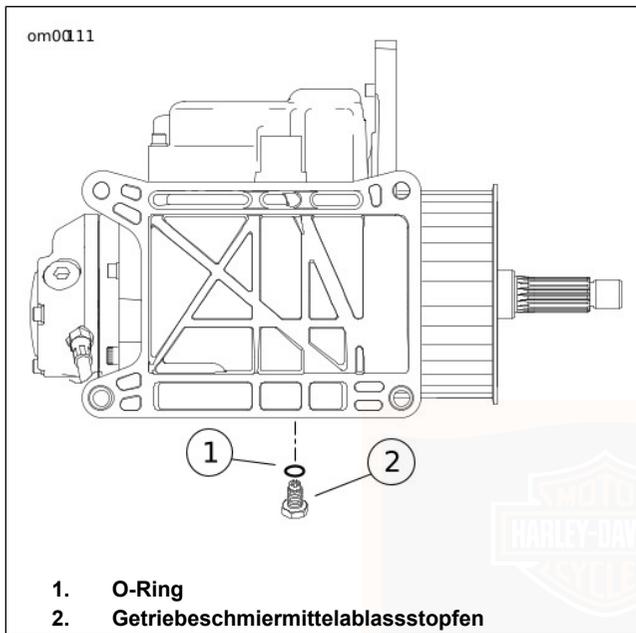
Getriebeschmiermittelablasstopfen und O-Ring
